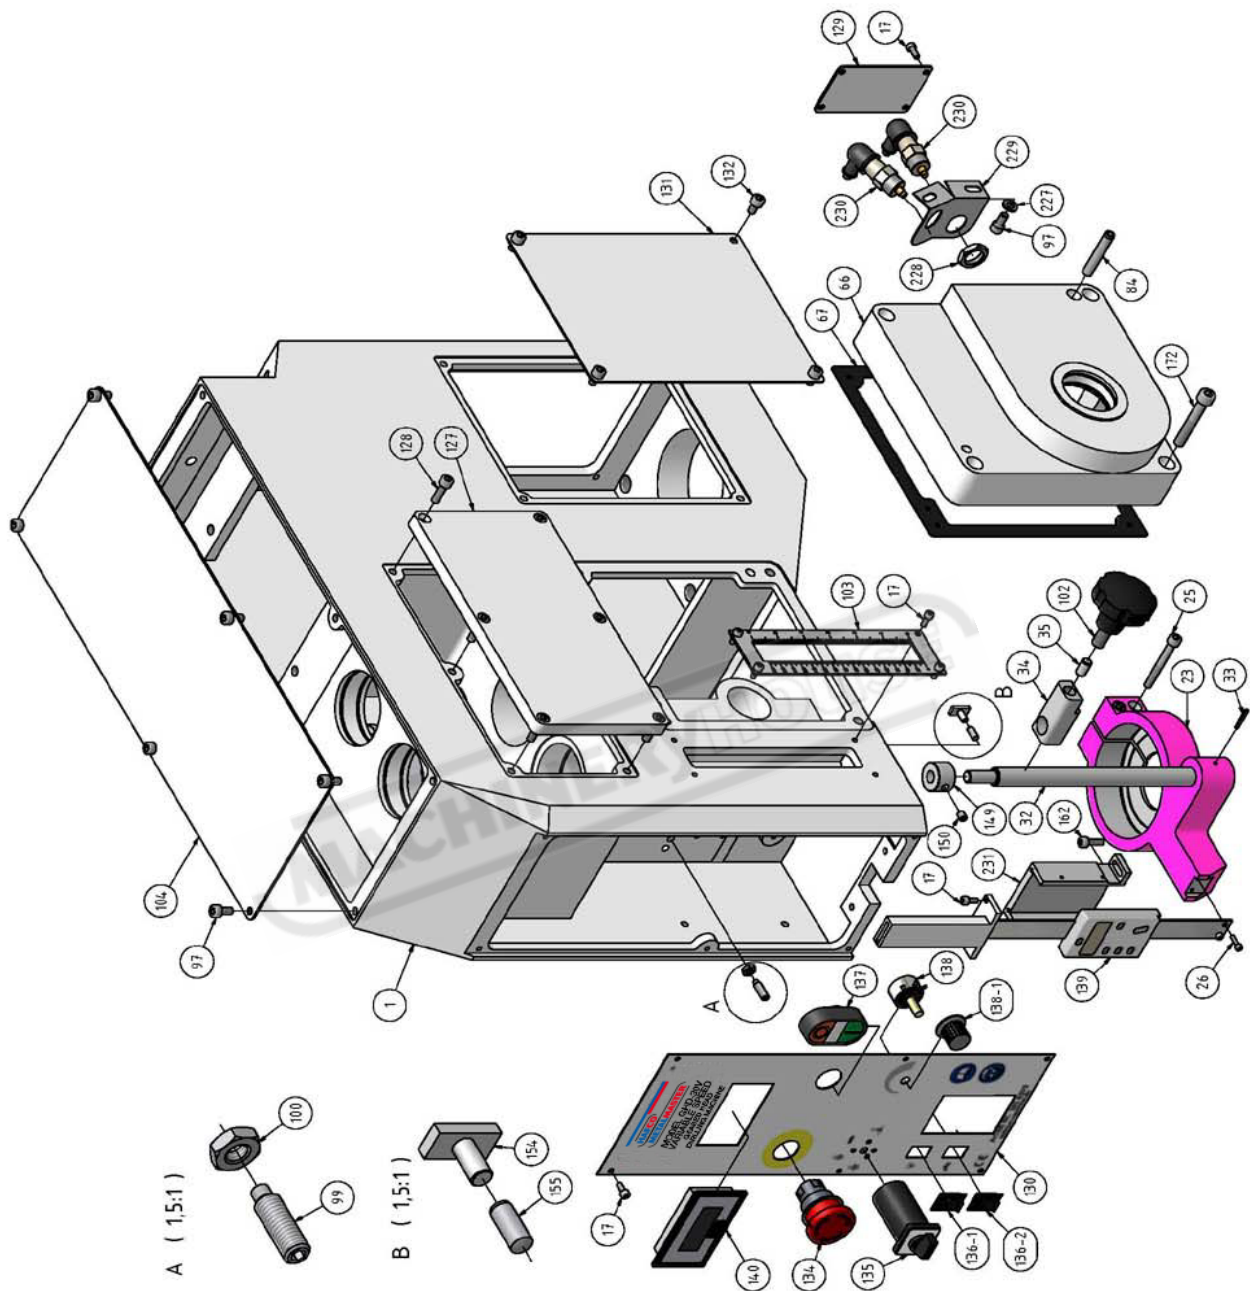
Bohrkopf 7 von 9 - Drilling head 7 of 9
